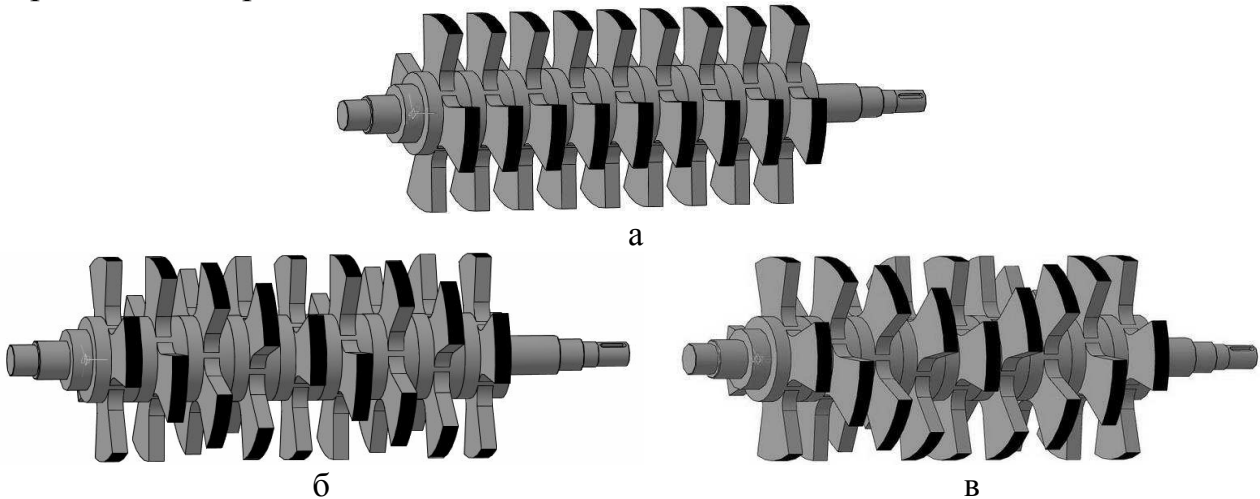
Типы роторов роторной зубчатой дробилки по расположению зубьев на валу: а – линейный, б – спиральный; в – шевронный
